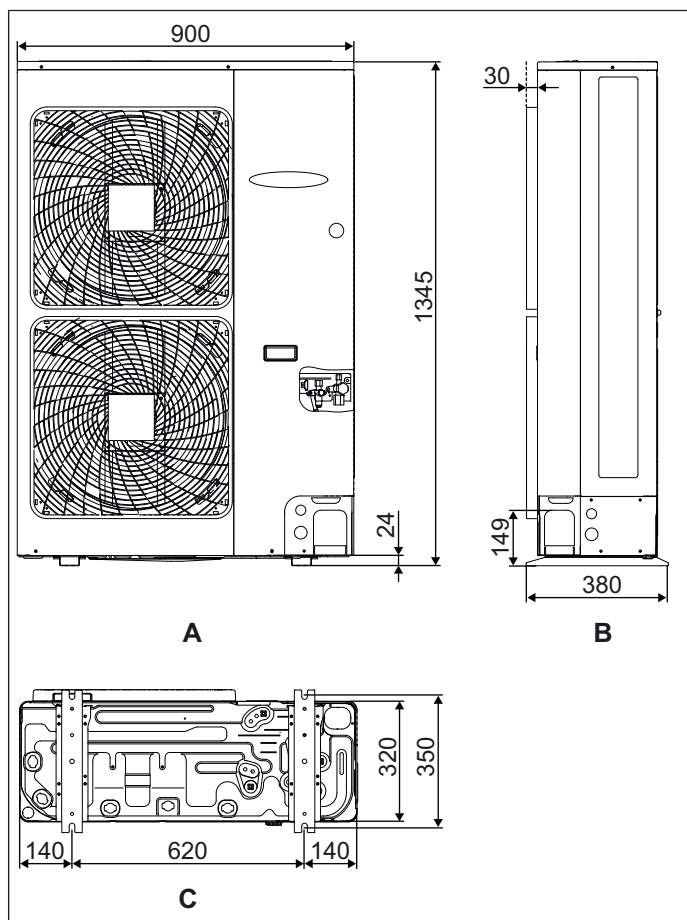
Abmessungen Außengerät RRLQ 11-16 kW
